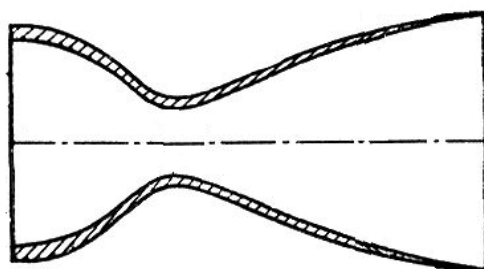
Схема сверхзвукового сопла Лавалья
